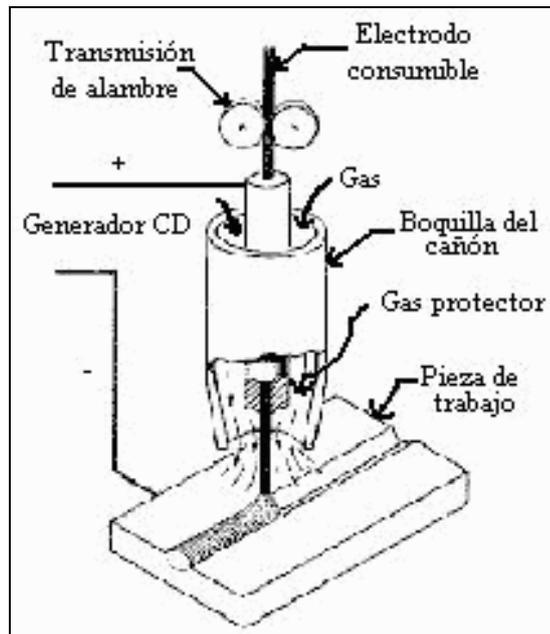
Diagrama esquemático de soldadura MIG³⁶.
